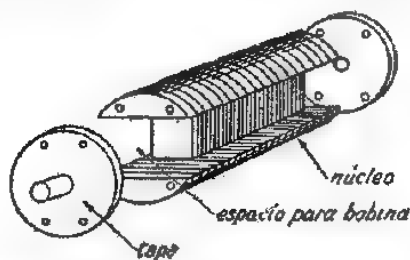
Despiece del inducido a rotor del magneto, en el que puede verse la cavidad para alojar el bobinado.
